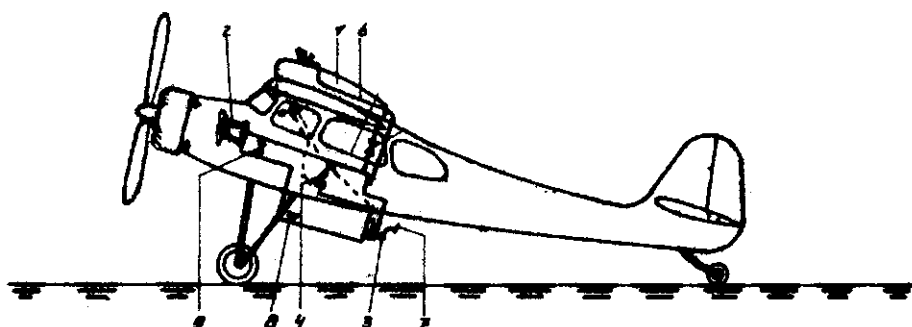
Schema van spuitinstallatie op Stinson Vigilant
